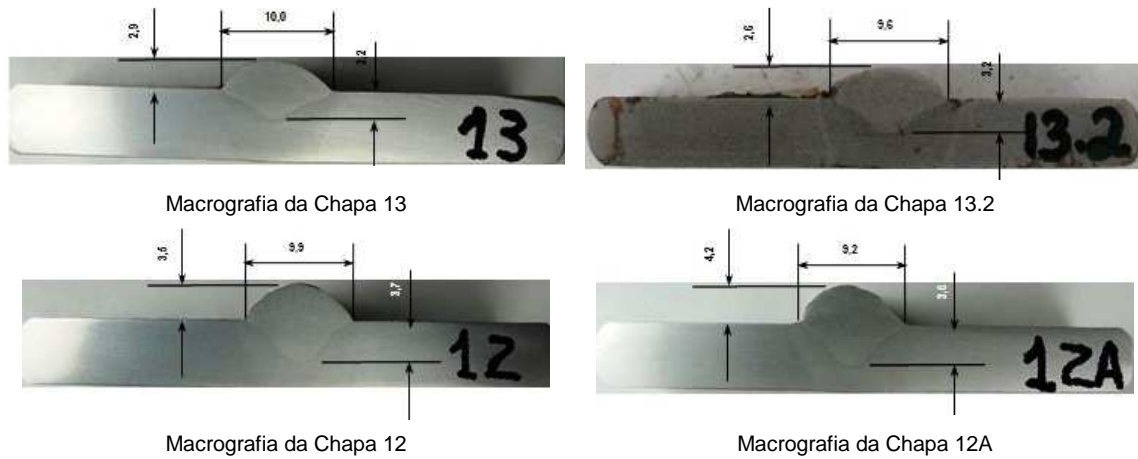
Macrografias com altura do reforço (r), largura do cordão de solda (b) e a penetração das soldas com $\text{CO}_2+6\%\text{H}_2$.
